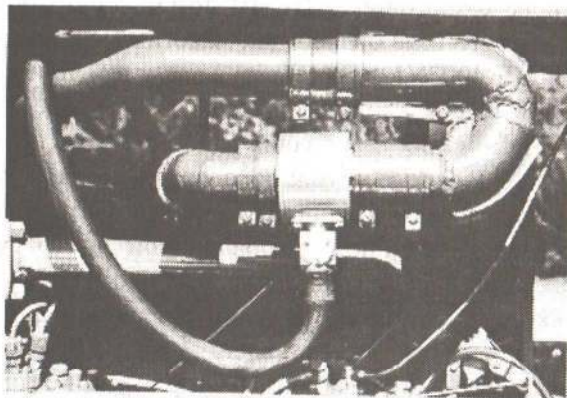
Вид на универсальный газовый смеситель-дозатор сварочной установки АДД-4002У1
